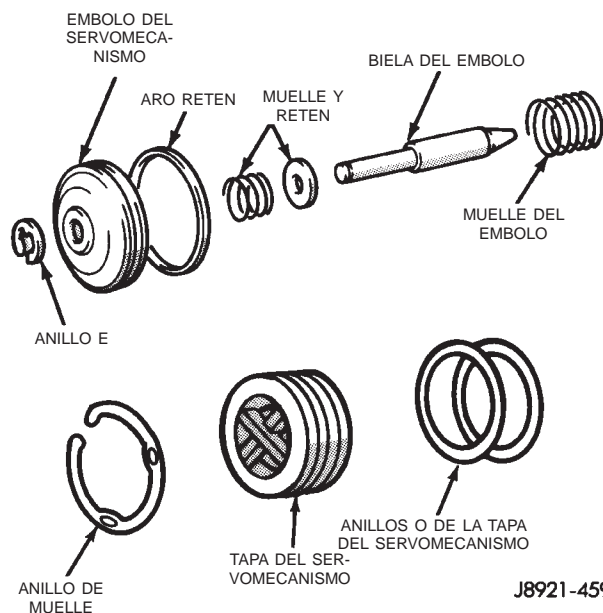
Componentes del servofreno de rodadura libre en segunda
